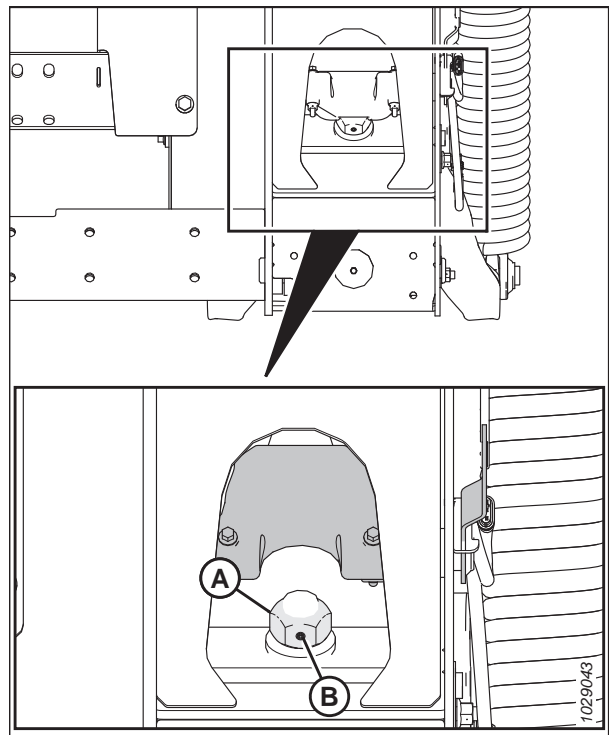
Dispositivo di bloccaggio flottazione – Destra
